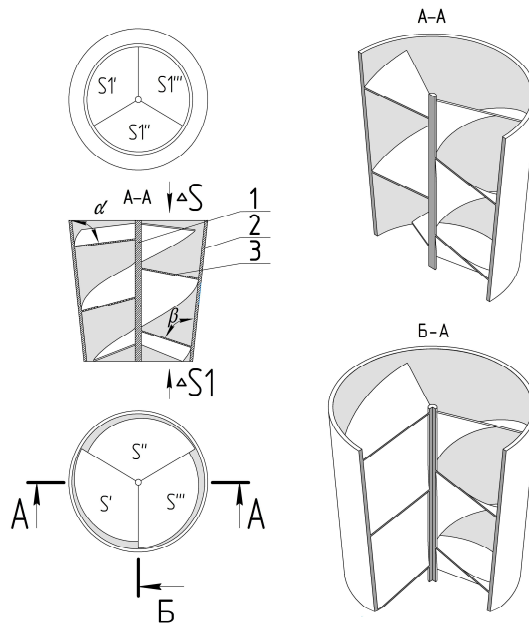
Схема турбіни з прямими спіралеподібними лопатями зі звуженням корпусу: 1 – вал, 2 – порожнистий циліндричний корпус, 3 – спіралеподібна лопать
